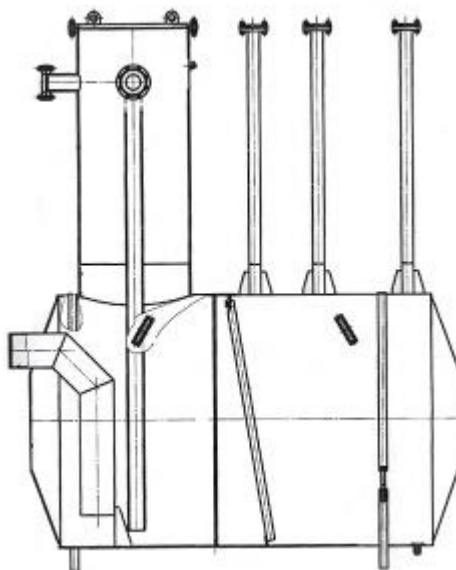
Эскиз общего вида резервуара ЕП-10-2000-1-2
